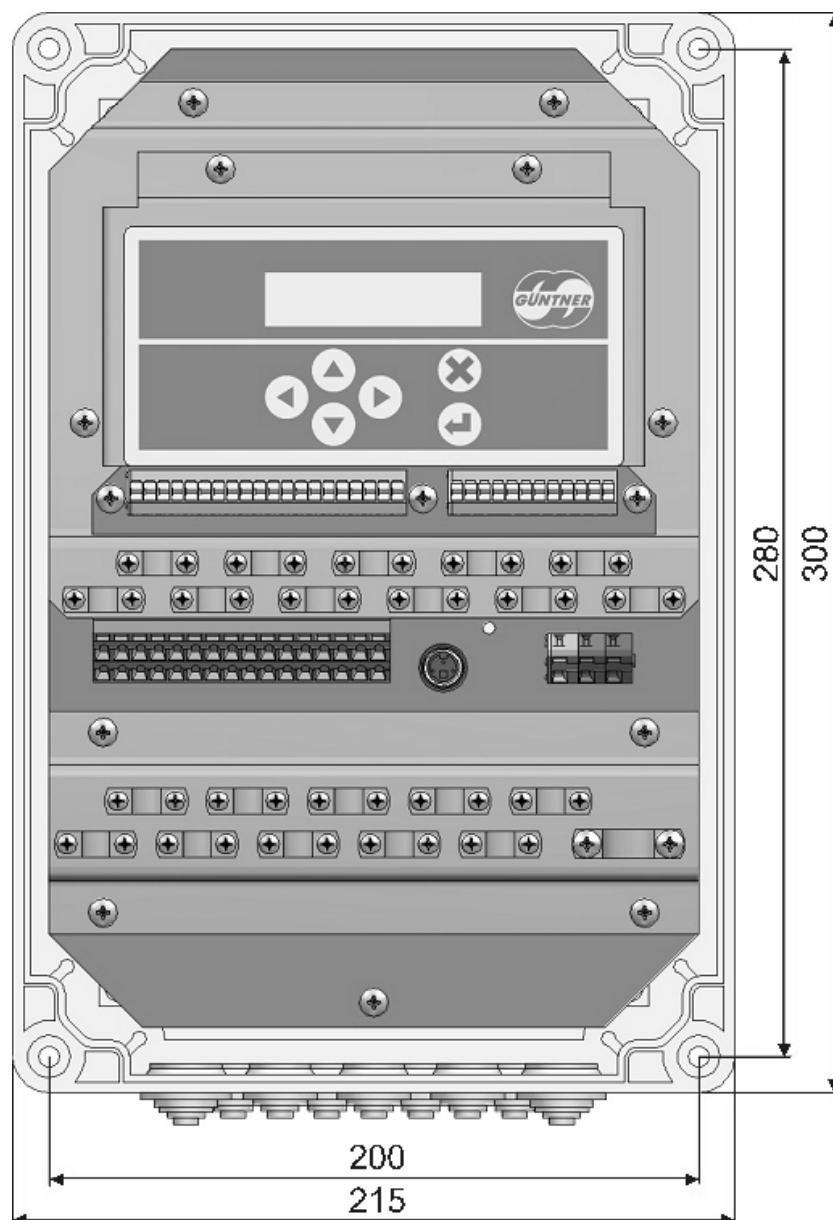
Dimensões de caixa GMM EC 01 / 04 / 08 (.1)
